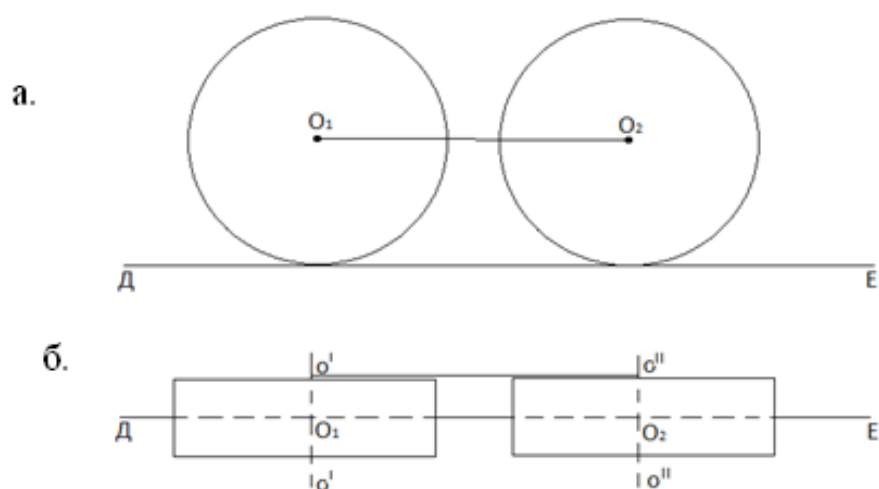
Схема пары цилиндрических колес: а.– вид сбоку, б.– вид сверху.
